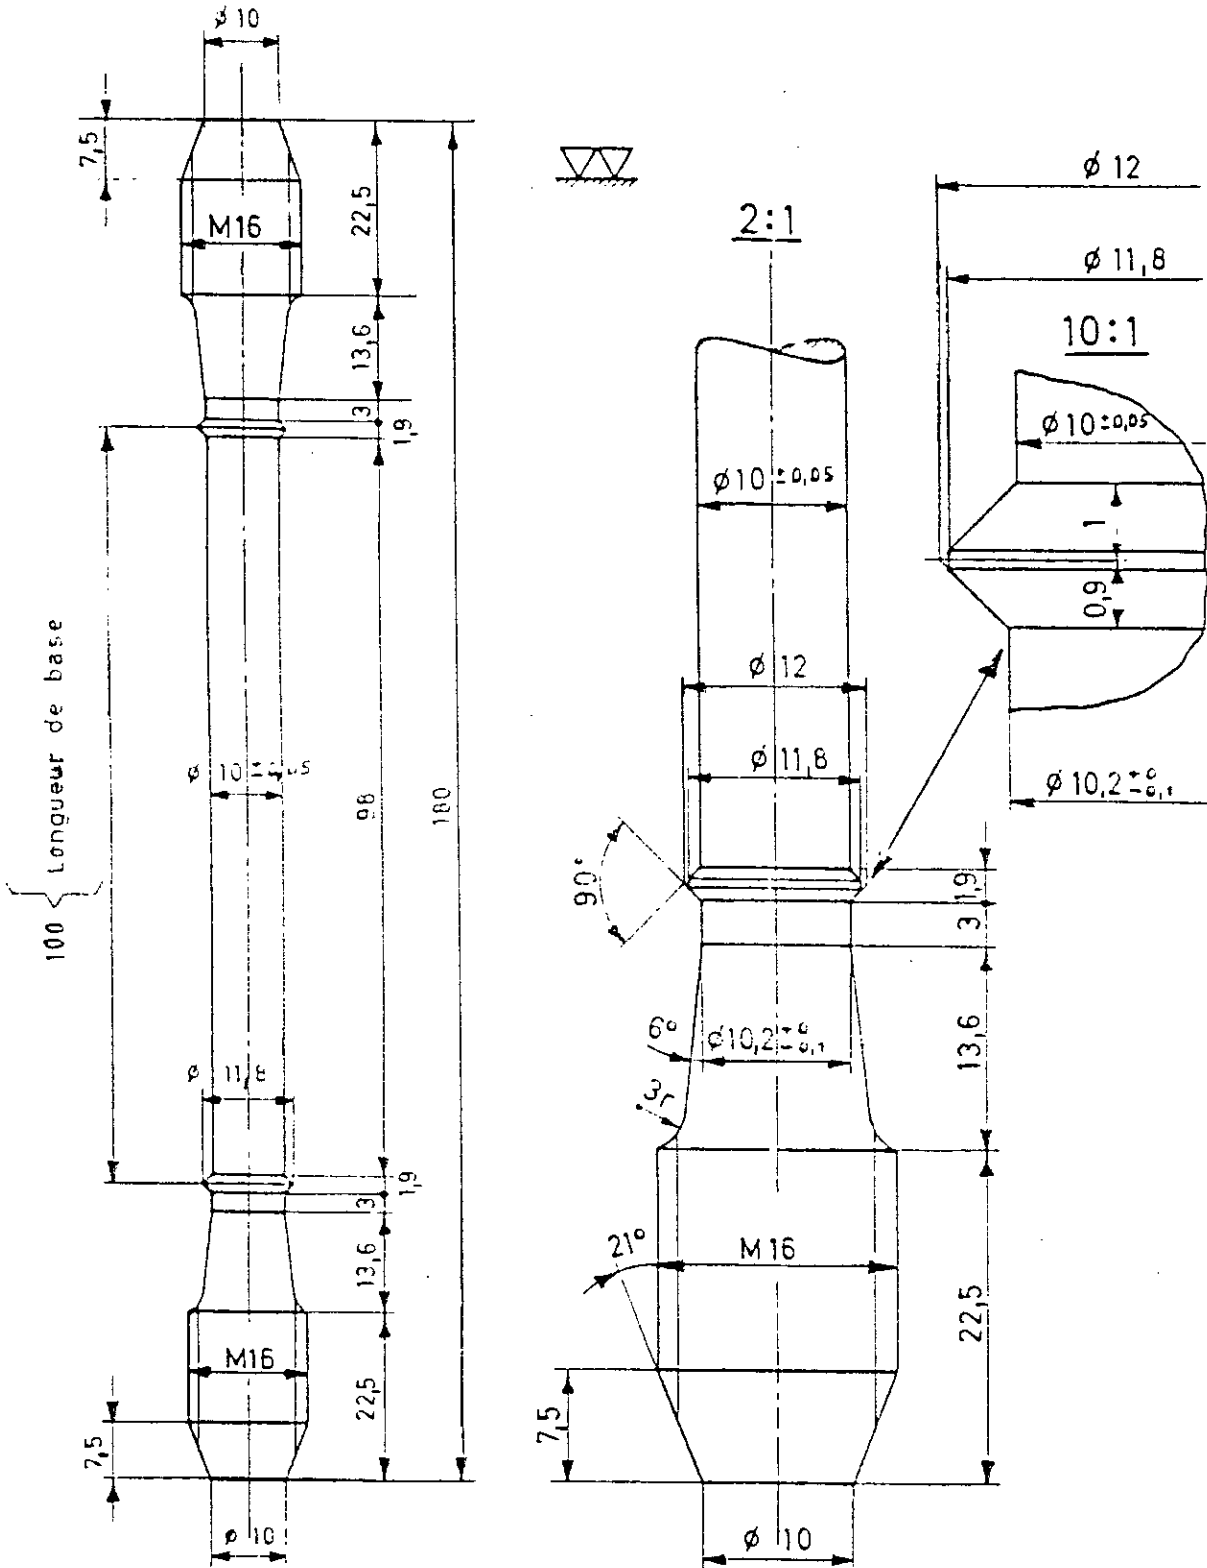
Epreuve pour machine de fluage (DIN 50125).
